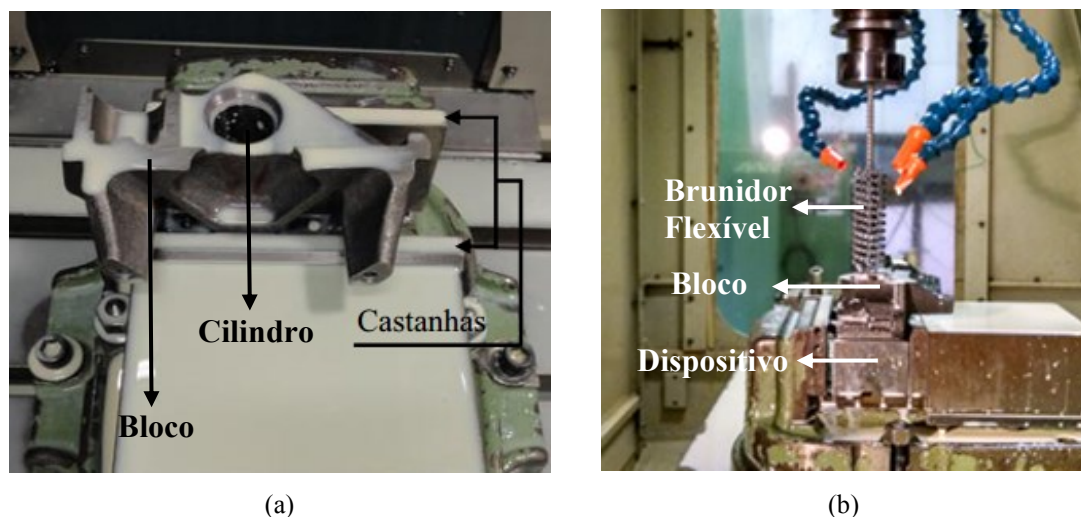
(a) Vista superior e (b) e vista lateral da fixação do bloco do compressor na máquina CNC.
